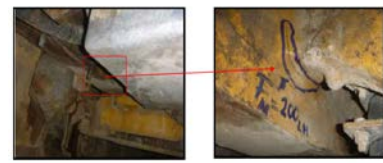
Tractor de orugas D11R y detalle de fisura detectada
